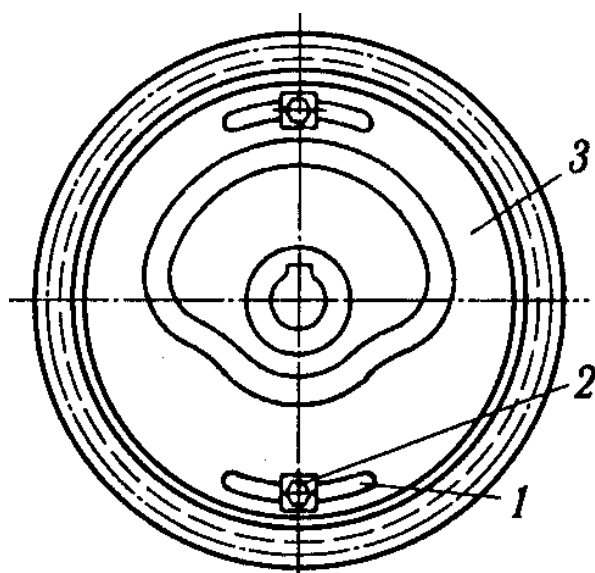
Схема кріплення копіра на шестерні колінчасто-важільного преса
